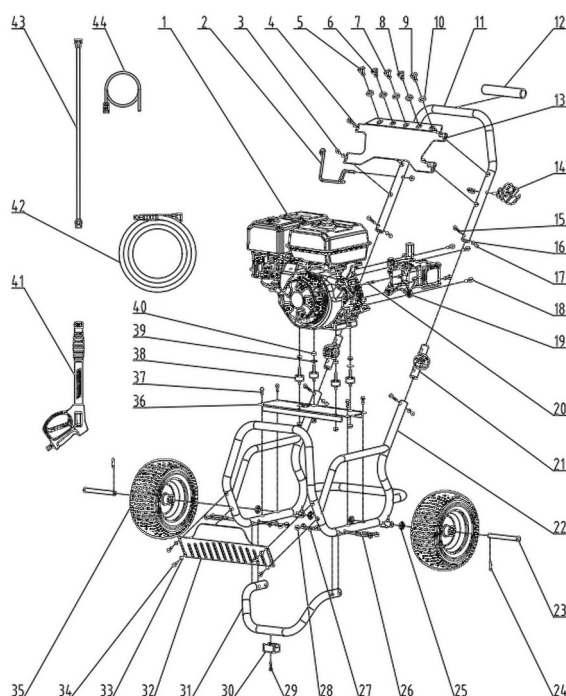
Vue éclatée de l'AY-265 KT (réf. 5419965)
